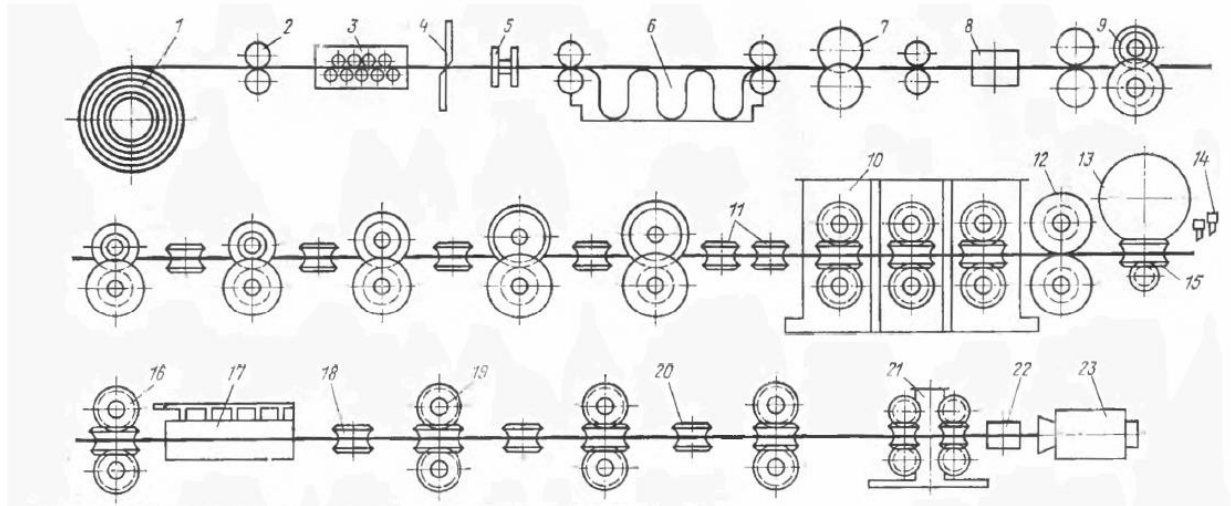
Типова схема розташування обладнання трубоелектрозварювального стану безперервного типу.
